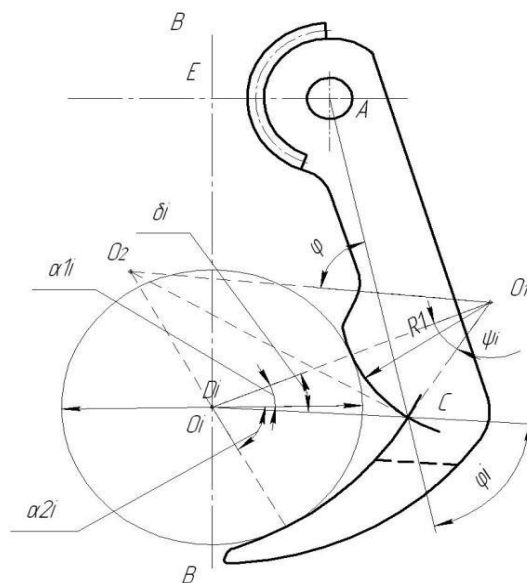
Конструктивная схема захвата с губками криволинейного профиля
